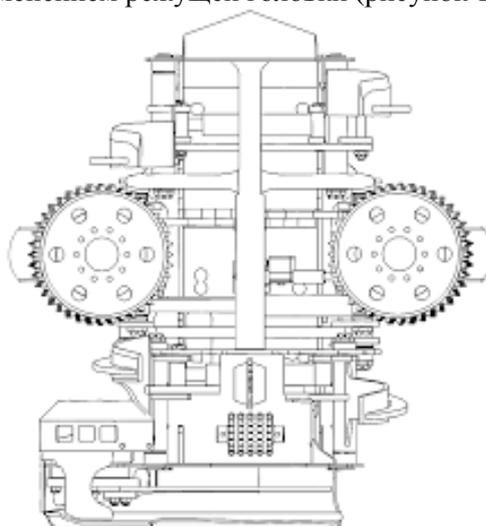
Режущая головка валочно-сучкорезно-раскряжевочной машины
